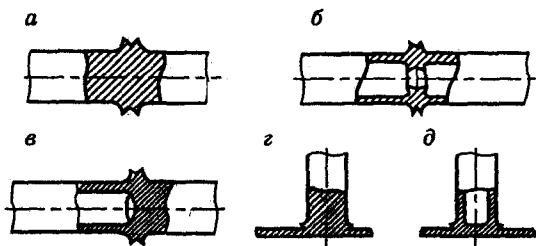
Типы соединений, выполняемых с помощью сварки трением:
